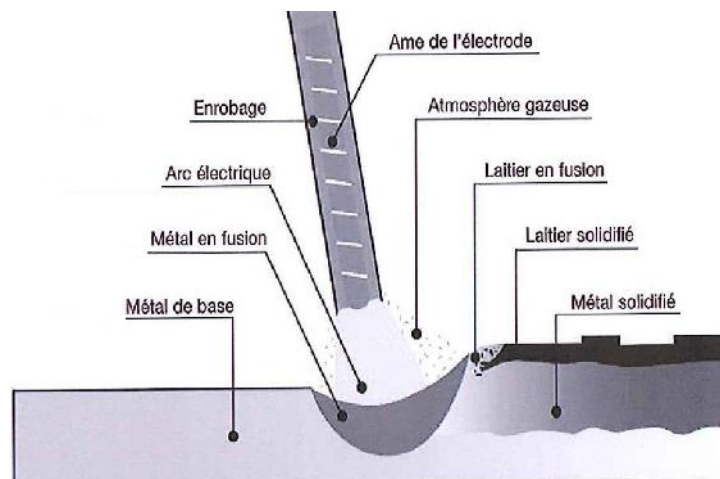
Schéma d'assemblage par soudage .
